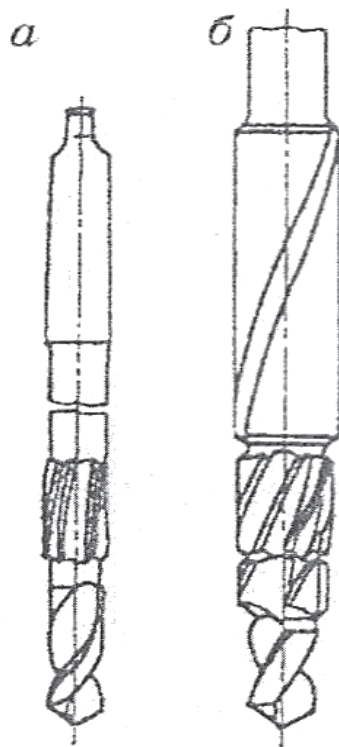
Сверло-развертка (а) и сверло-зенкер-развертка (б)
